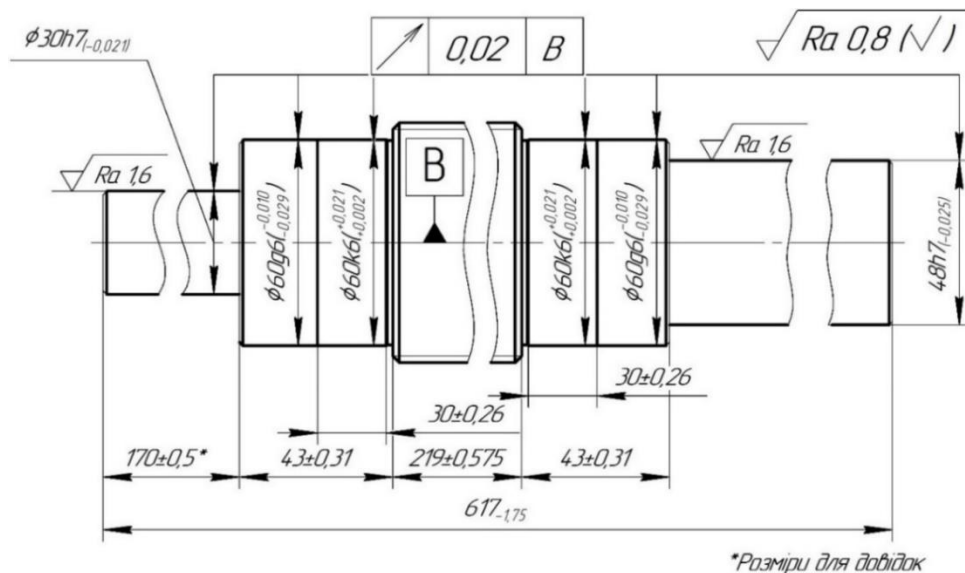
Ескіз заготовки на операції 035 «Круглошліфувальна»
